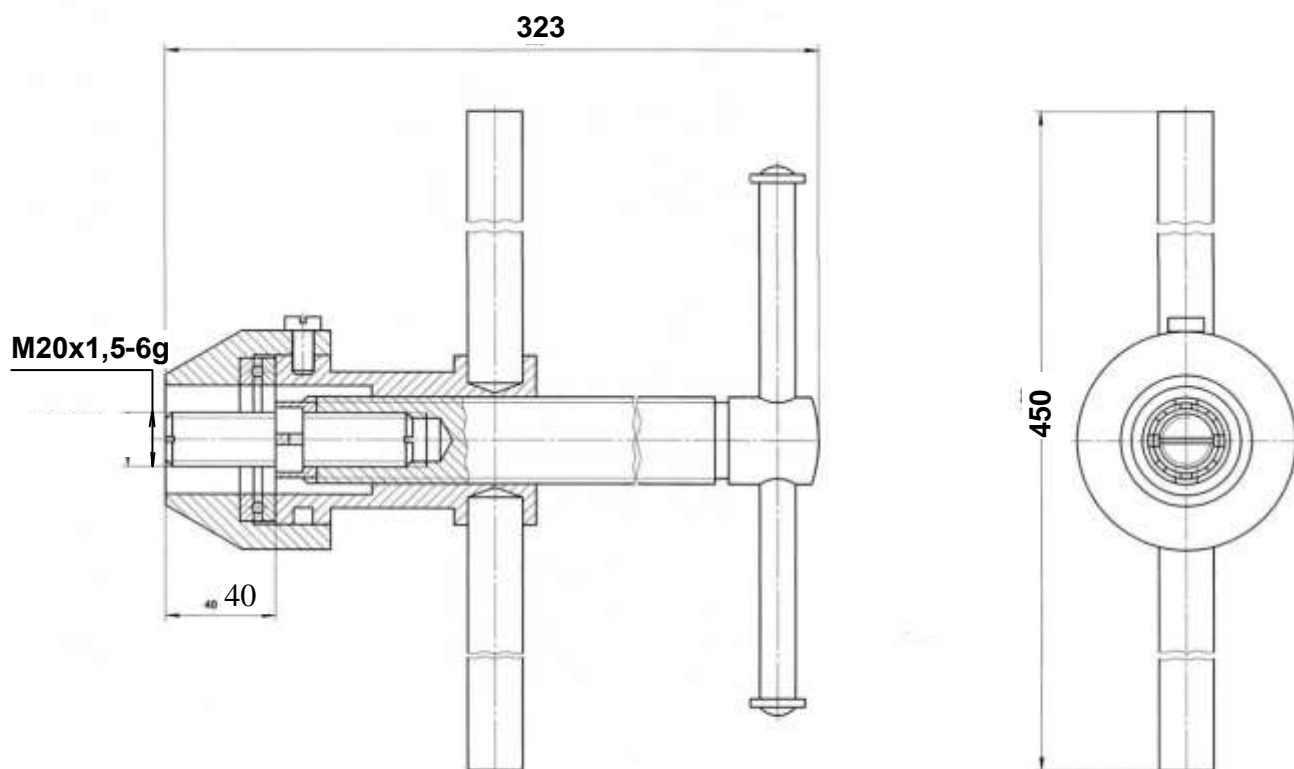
ЗМ 7823-4291-04 Приспособление для напрессовки шкива на коленчатый вал
